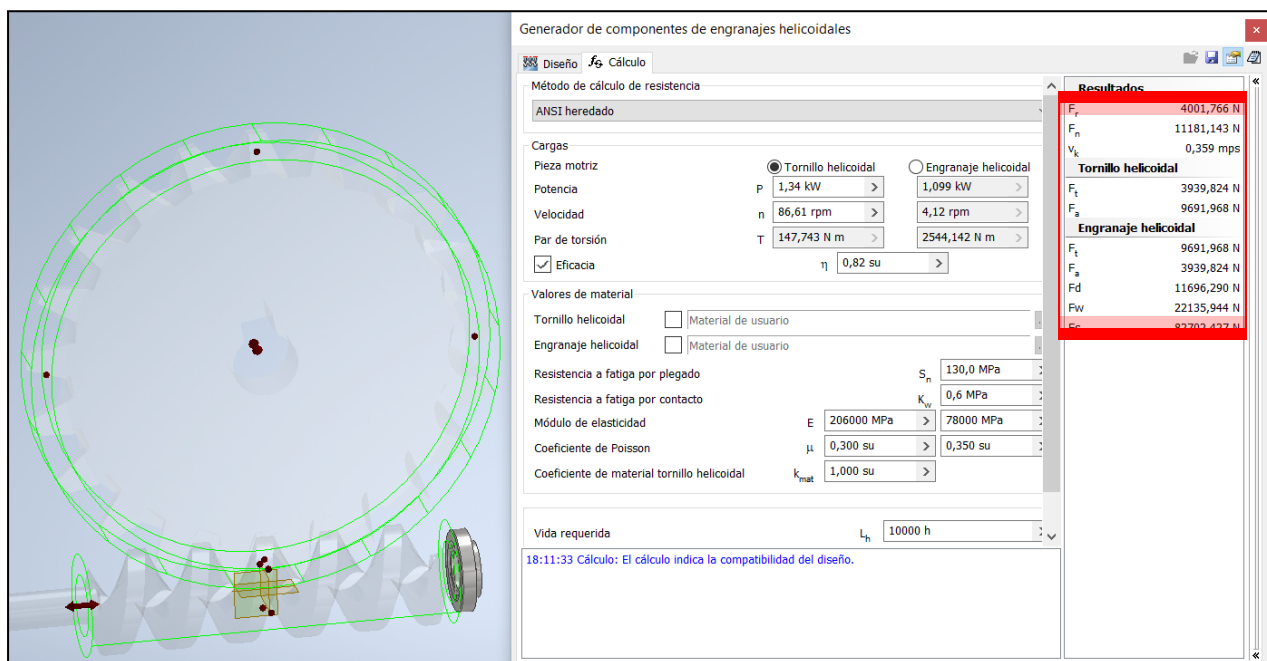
Fuerzas que se desarrollan en el sistema de potencia Engranaje-Tornillo sin fin. *Realización propia.
